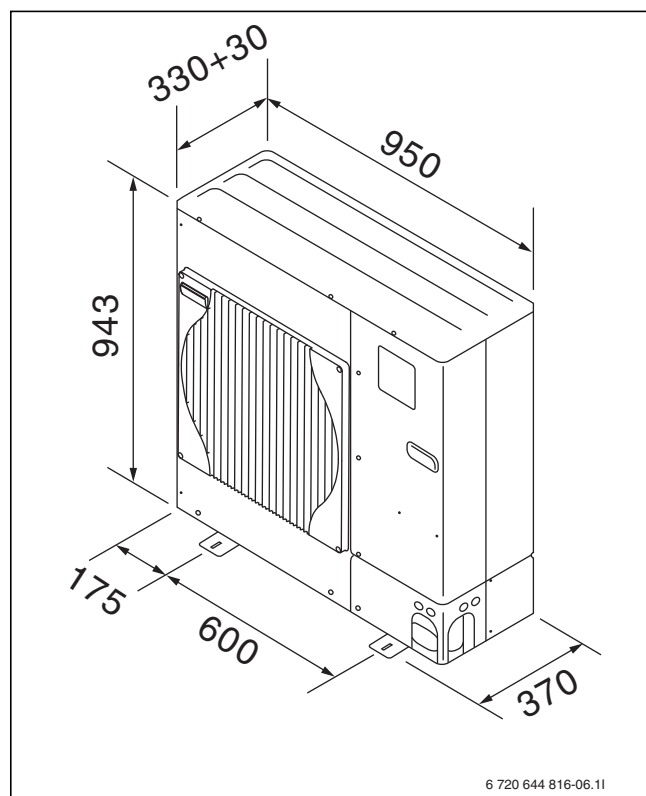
Dimensioni unità esterna ODU 7,5 (misure in mm)
